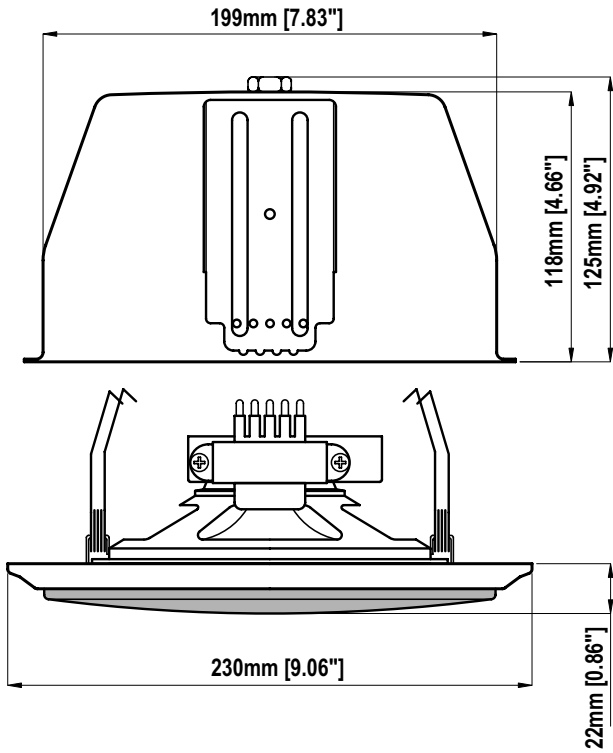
Dimensioni • *Dimensions* • Dimensions • *Abmessungen* • Dimensiones
